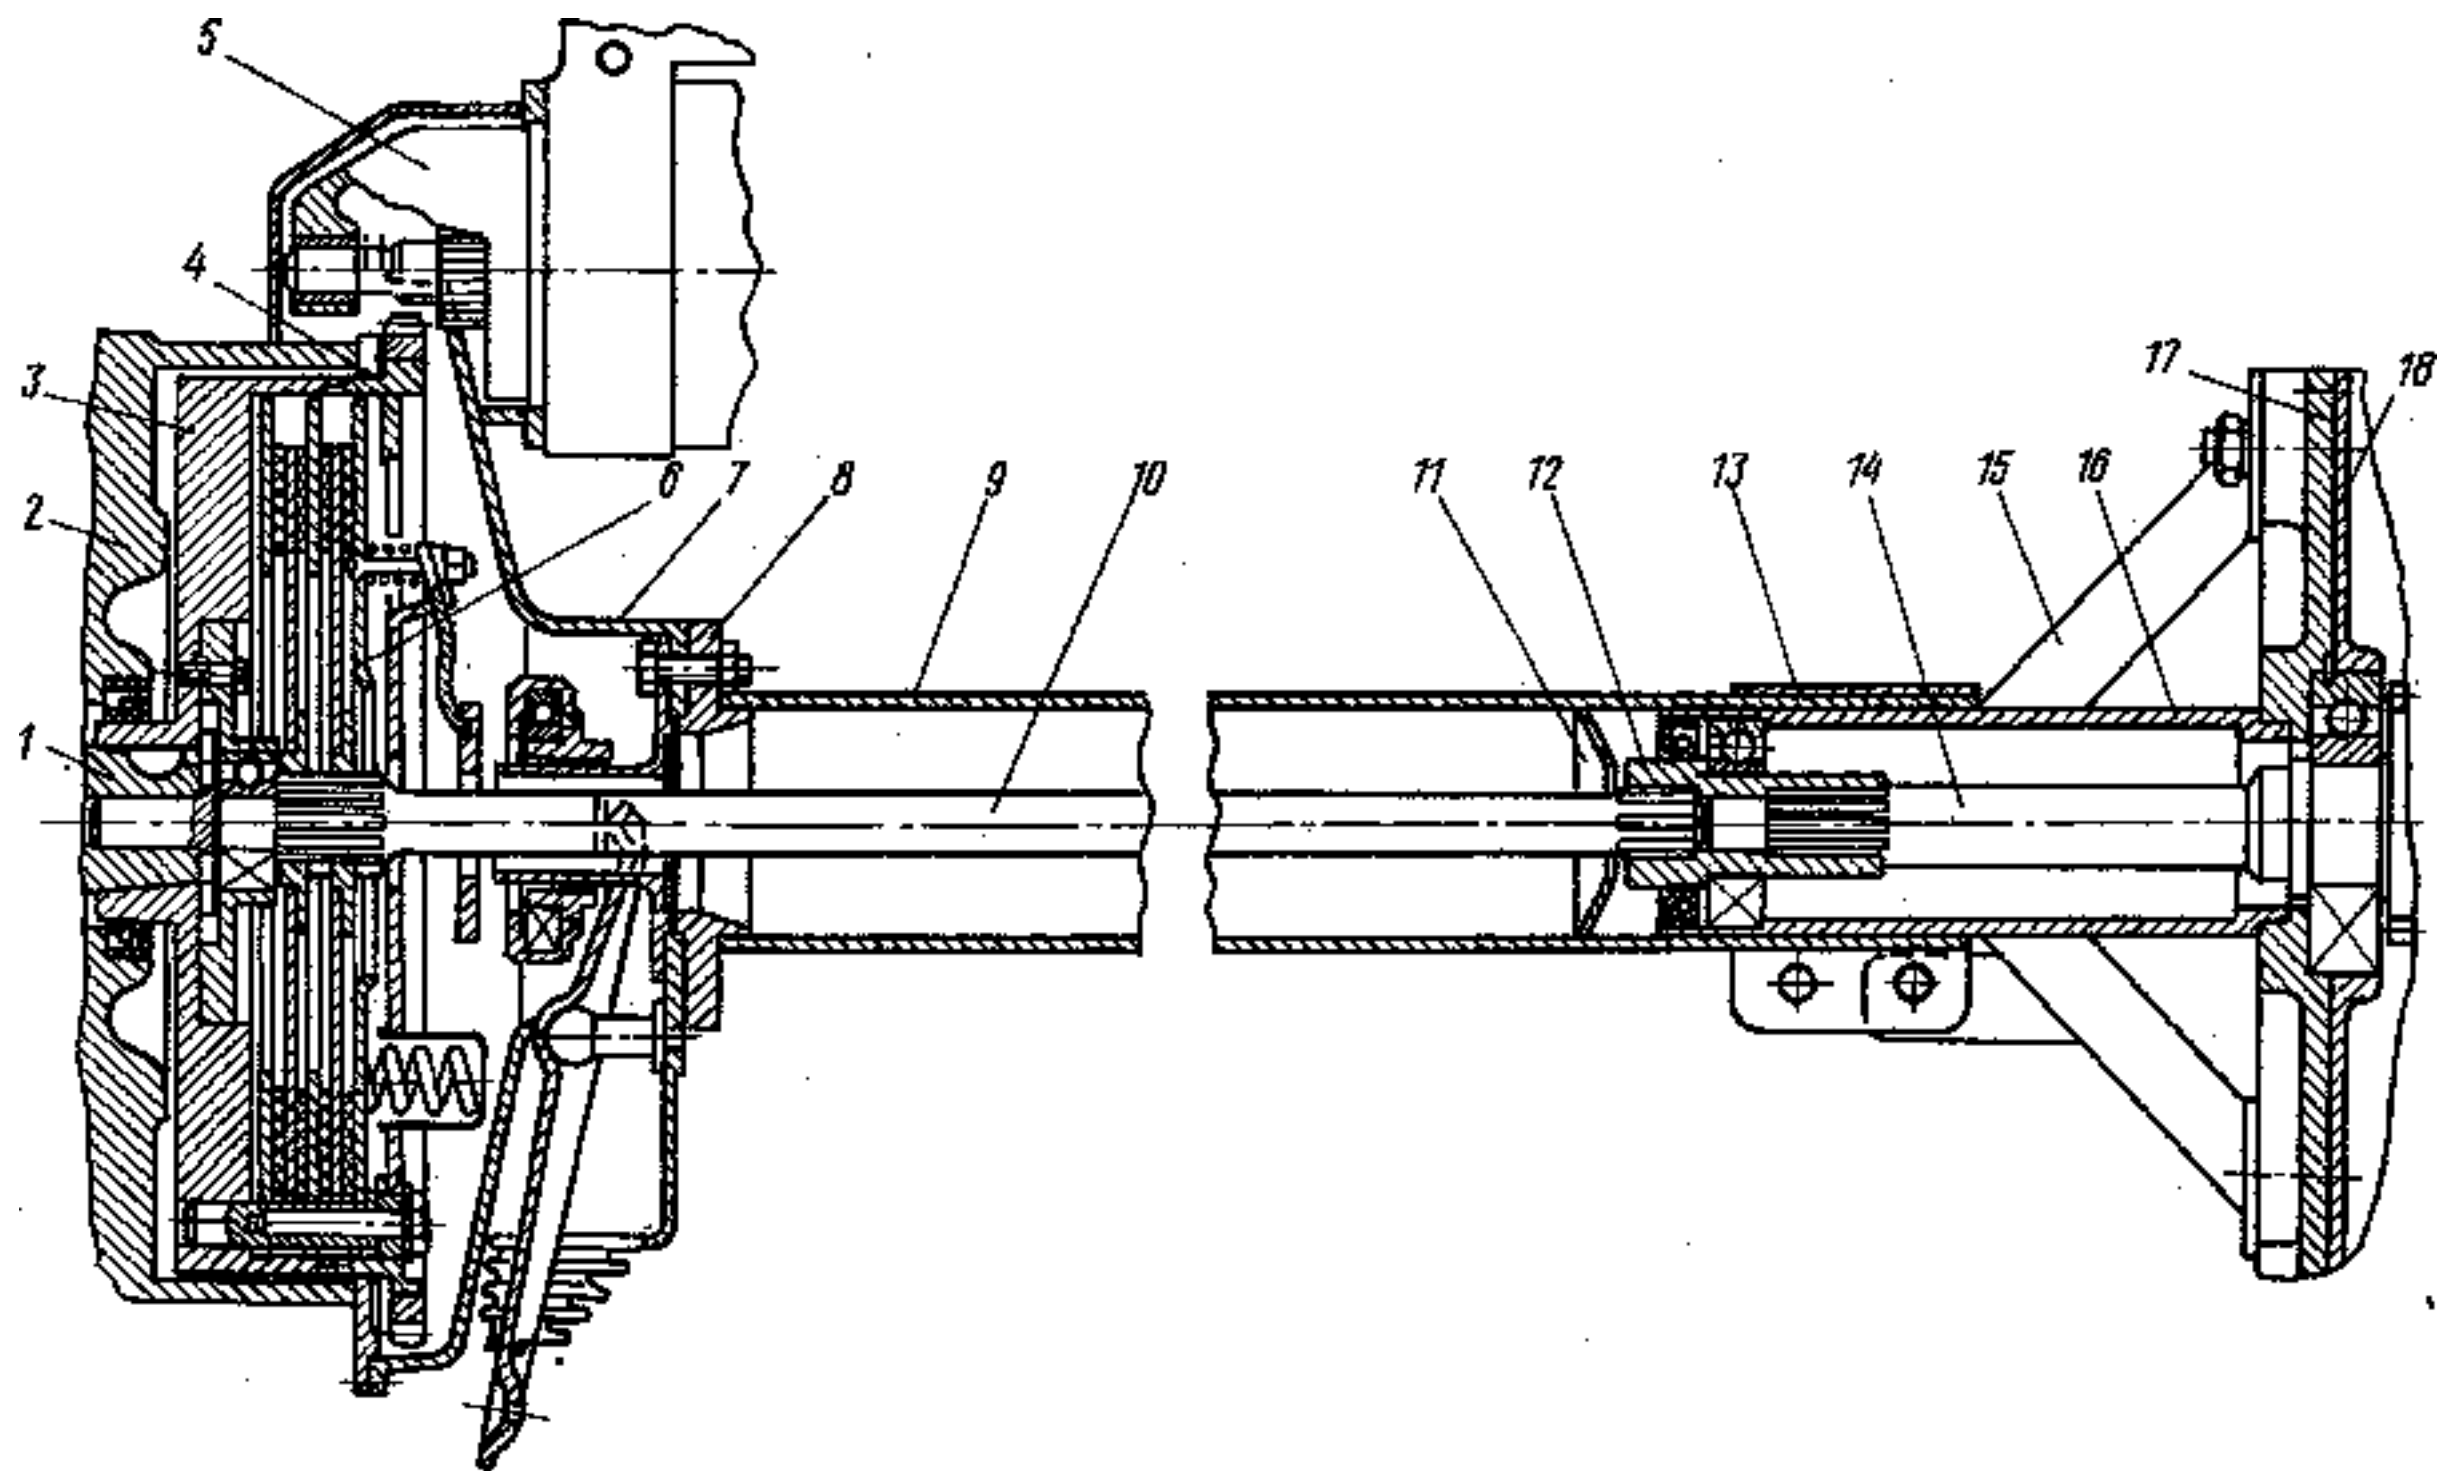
Соединение двигателя с коробкой передач с использованием удлинительного вала:
